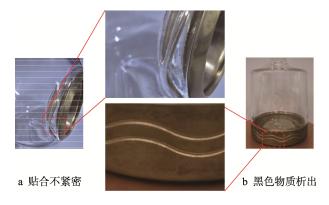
黄铜-玻璃成型件缺陷 Fig.6 Defects in formed parts of brass and glass
